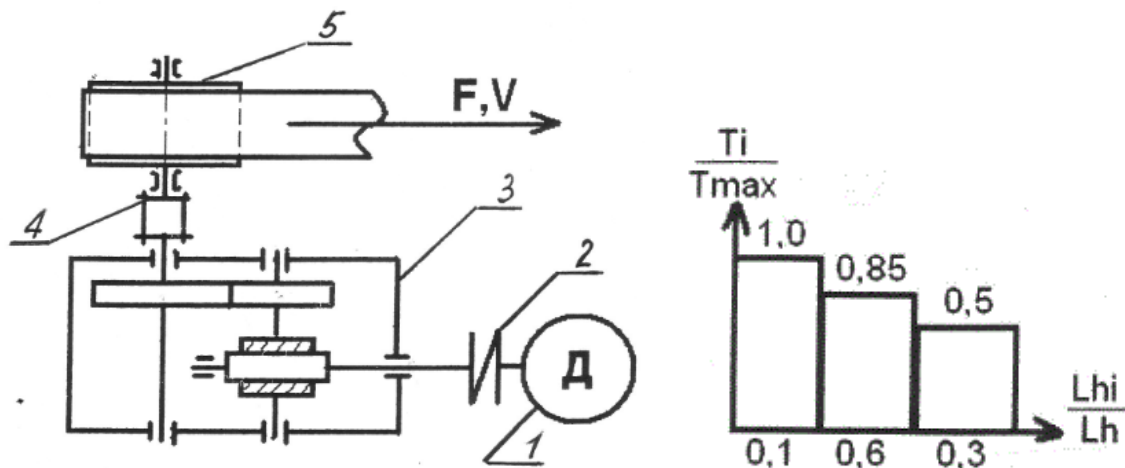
Схема двухступенчатого червячно-цилиндрического редуктора
